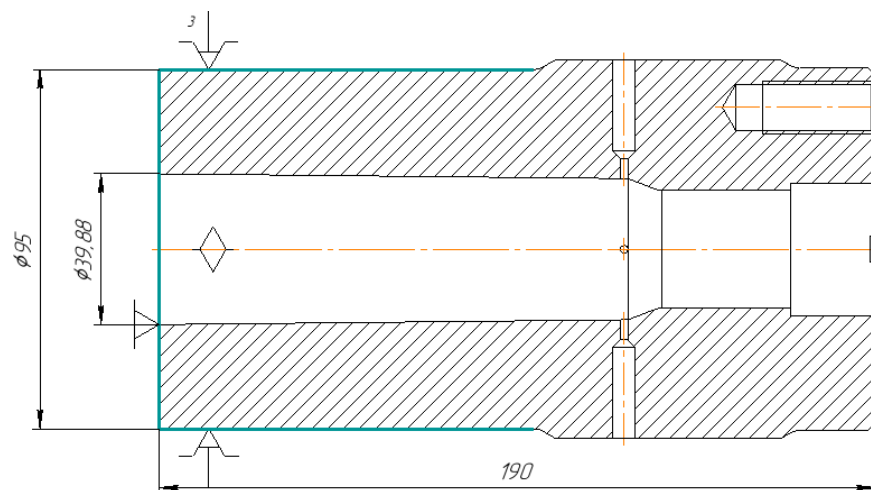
Схема базування деталі “Форма ” в пристосуванні
